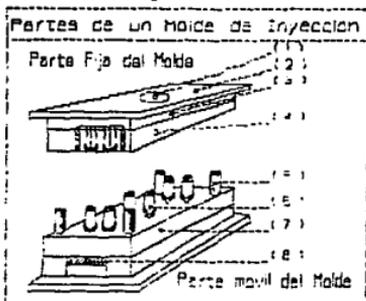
PARTES DE UN MOLDE DE INYECCION.
